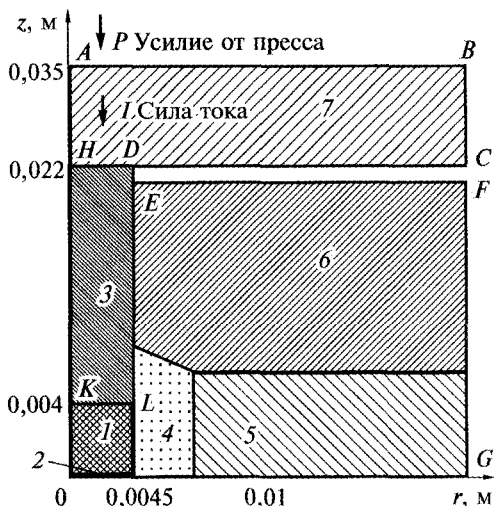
Схема технологического узла для спекания под давлением порошковых заготовок: 1 — заготовка из порошка титана; 2 — медная фольга; 3 — пуансон (сталь A12); 4 — контейнер из литографического камня; 5, 6 — элементы матрицы (сталь 40); 7 — плита пресса (сталь 40)
